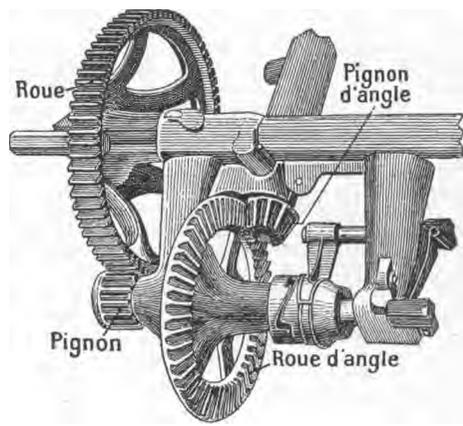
Les deux principaux types d'engrenages : engrenage droit et engrenage d'angle.
